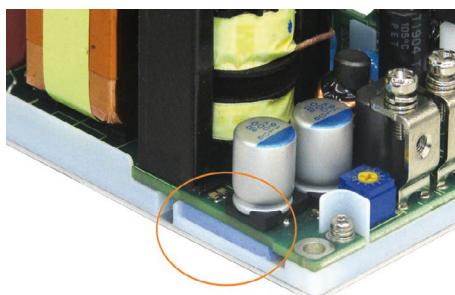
„Lückenfüller“ zwischen Leiterplatte und Gehäuse
